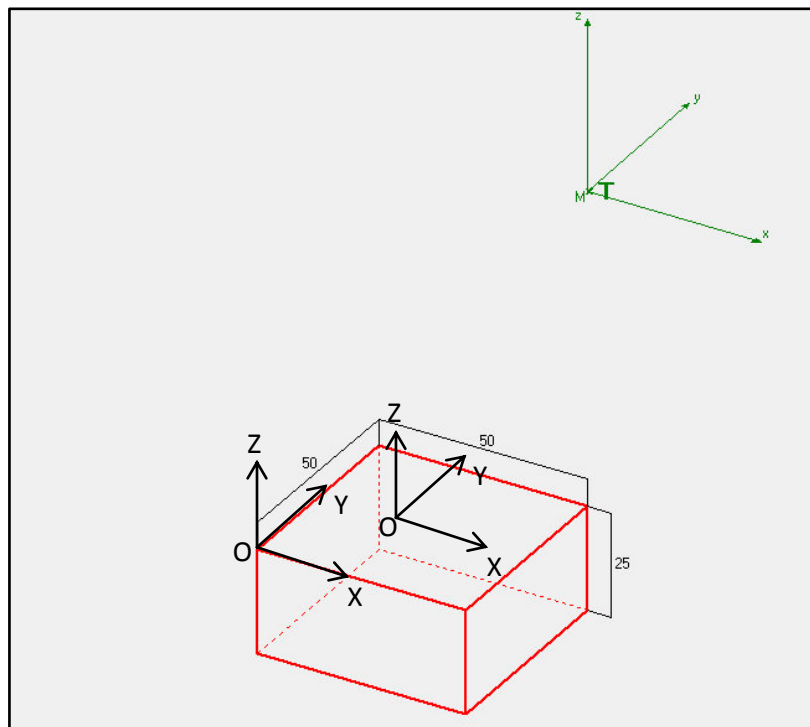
Cero máquina y el cero pieza del centro de mecanizado CNC
